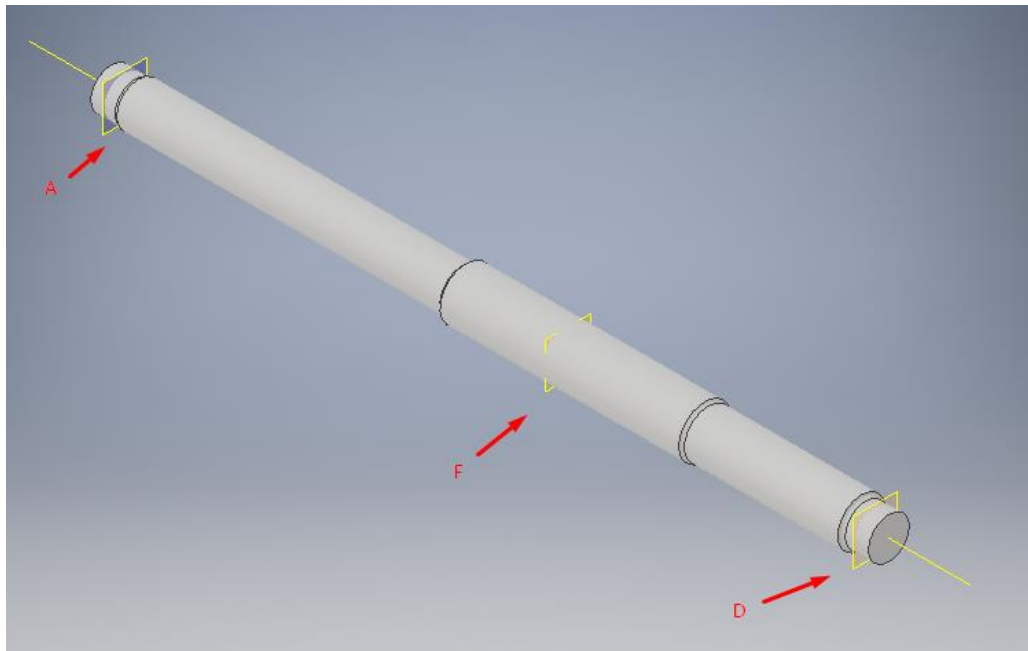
Vista del eje con los 3 planos auxiliares necesarios: A y D para los apoyos y F la sección de aplicación de la fuerza.
